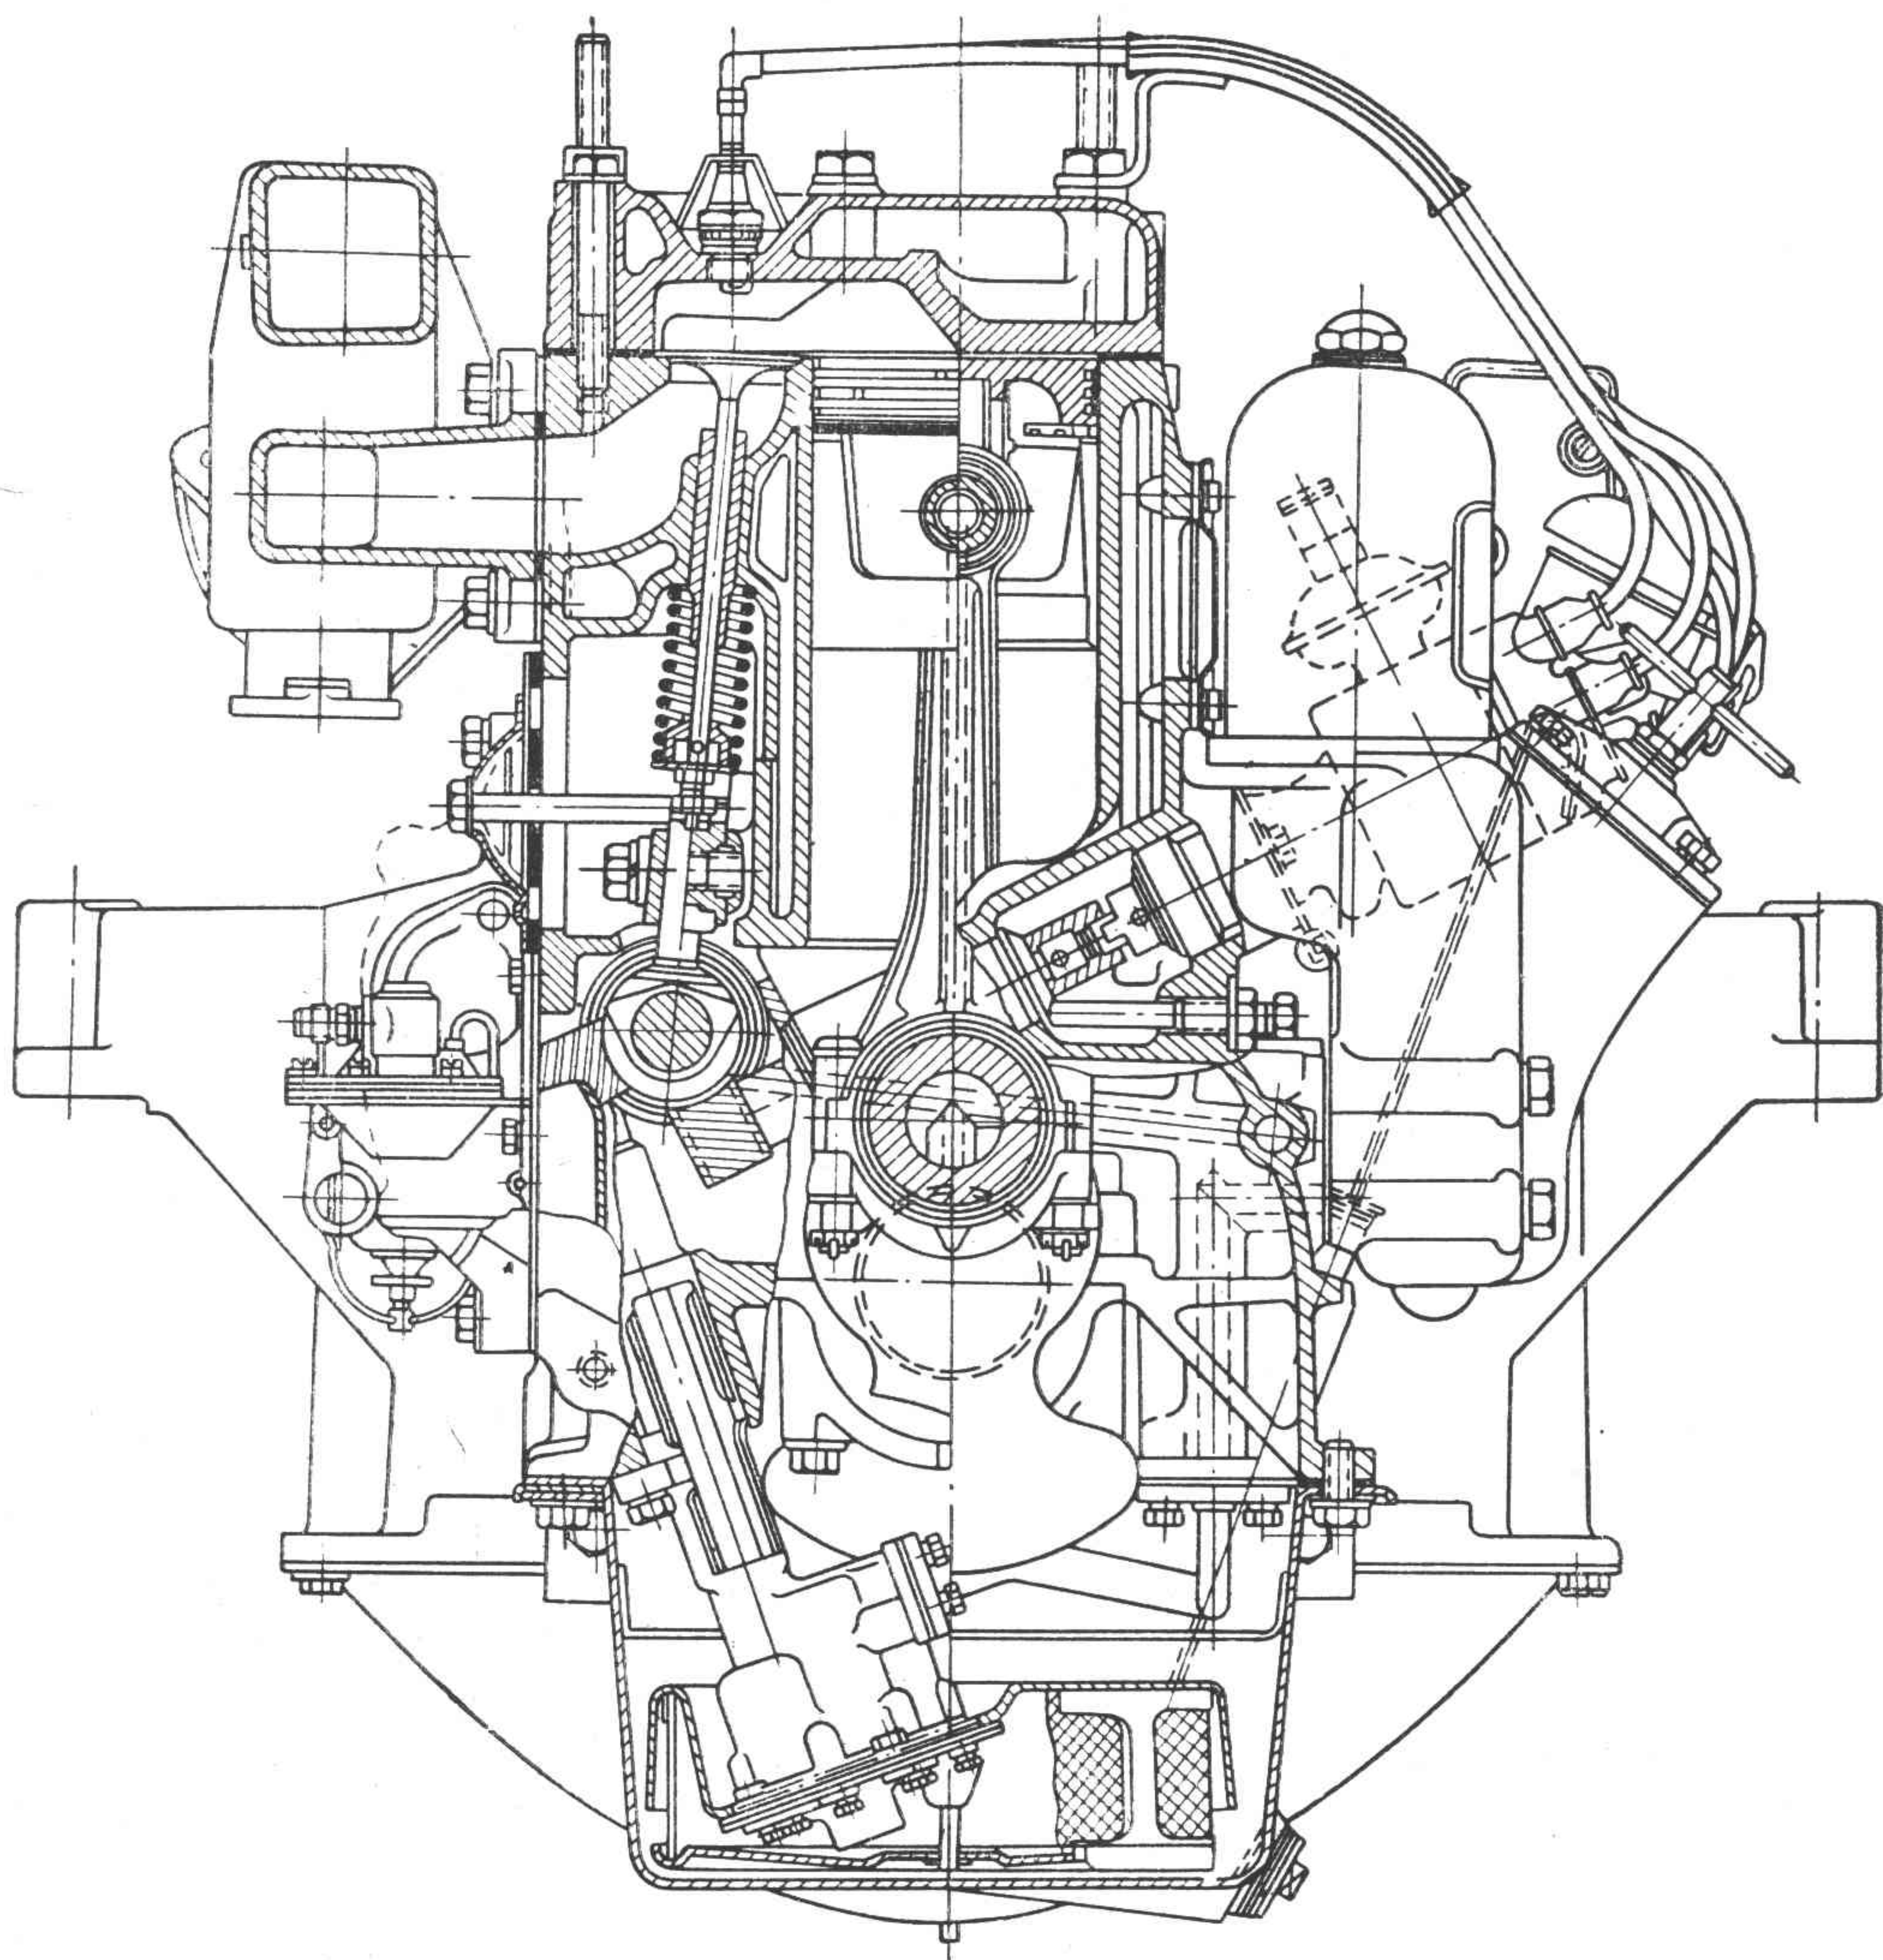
Поперечный разрез двигателя ЗИЛ-120
